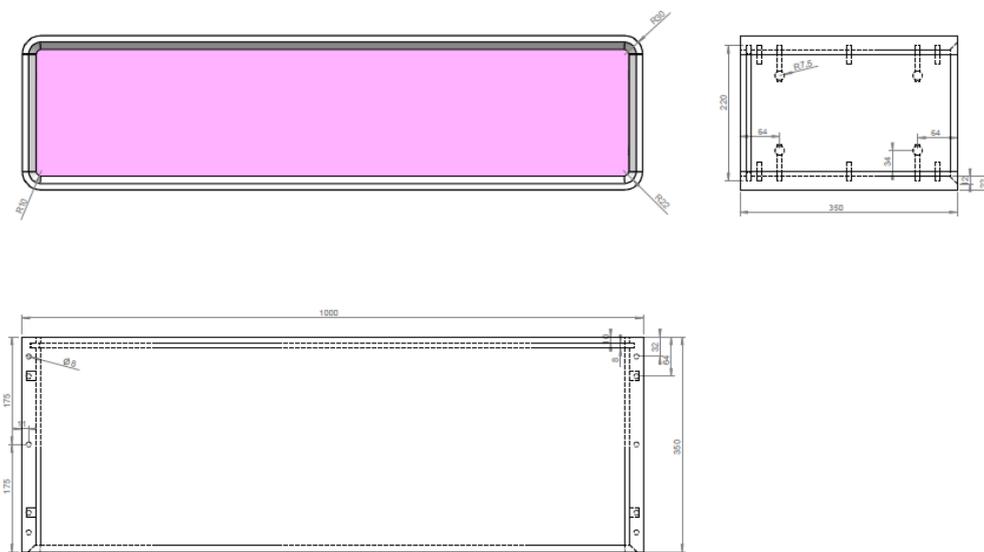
Imagem bidimensional da parte superior do móvel auxiliar.
